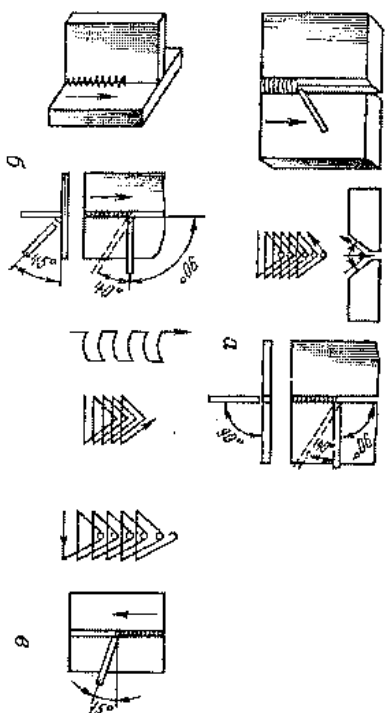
Положение и движения электрода при сварке в вертикальном положении:
